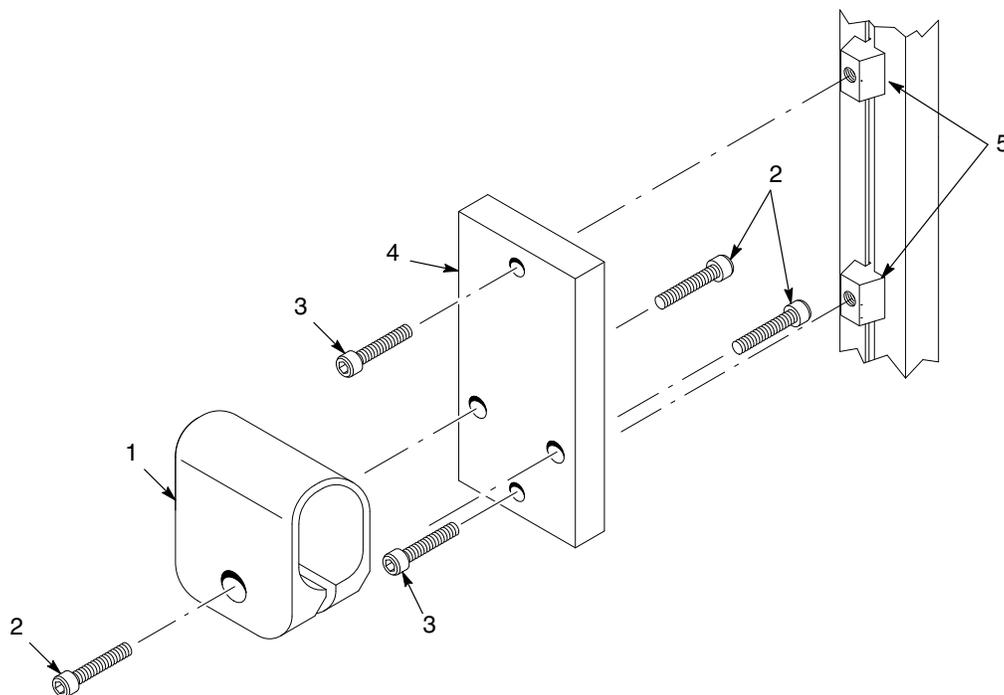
Conjunto de suporte deslocável, para pistolas com tubo de suporte
